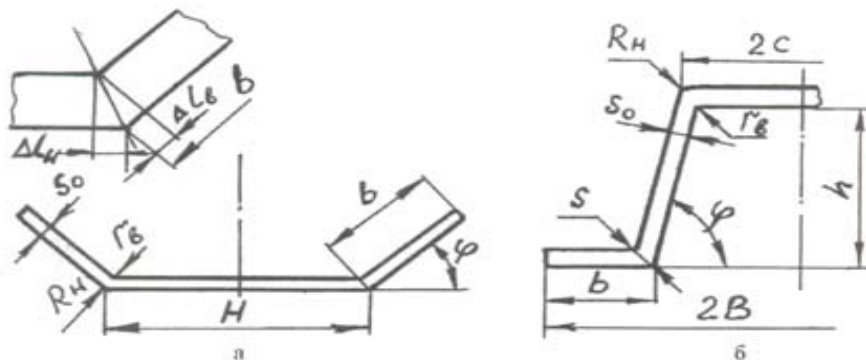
Геометрические параметры расчета ширины заготовки профилей: а – швеллерного; б – корытообразного
